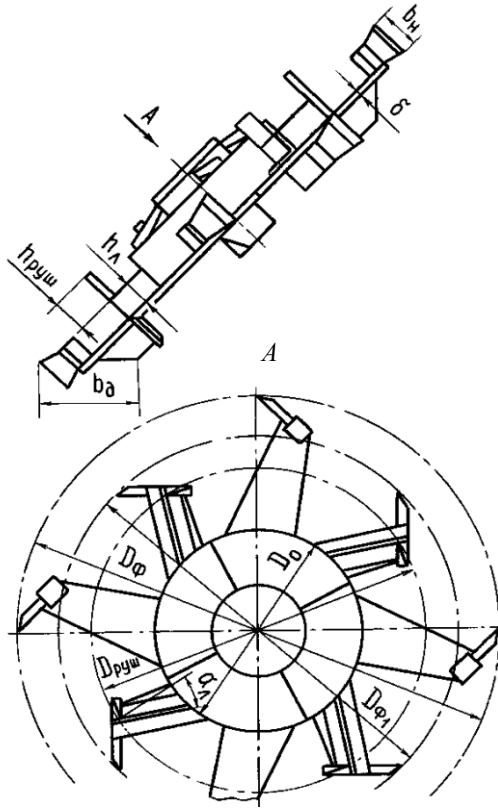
Фреза плужно-фрезерного каналокопателя
